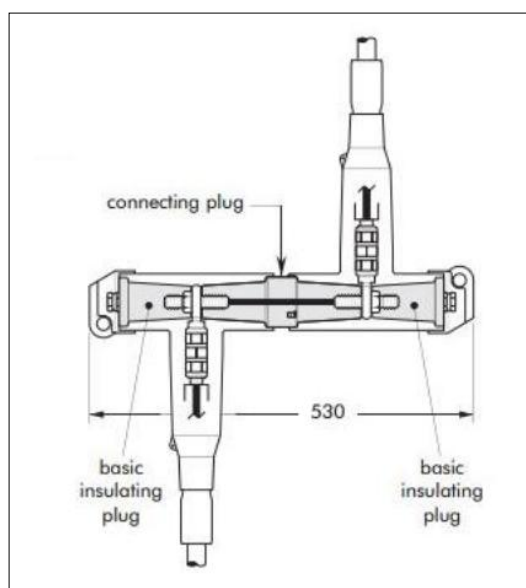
Dettaglio giunzione tra cavi MT all'interno del pozzettone di sezionamento
